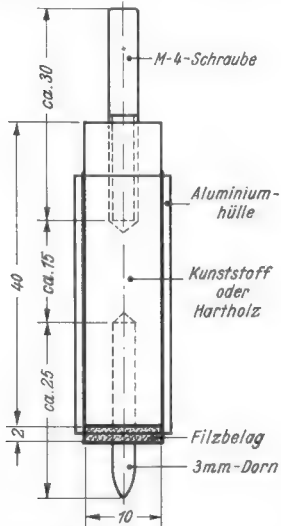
Werkzeug zum Blankreiben von Masseverbindungspunkten
